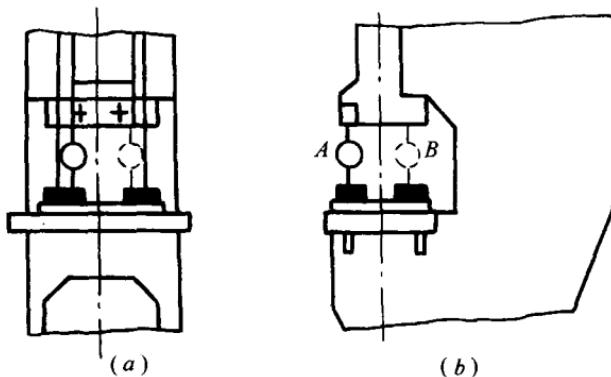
检验滑块下平面对工作台板上平面的平行度
